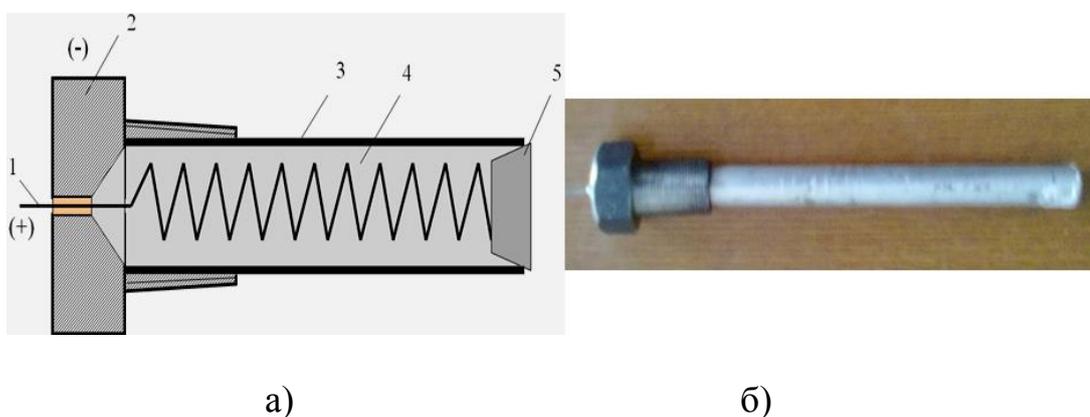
Устройство для разогрева моторного масла: а – схема устройства; б – внешний вид устройства; 1 – спираль; 2 – штуцер; 3 – корпус; 4 – кварцевый песок; 5 – пробка
